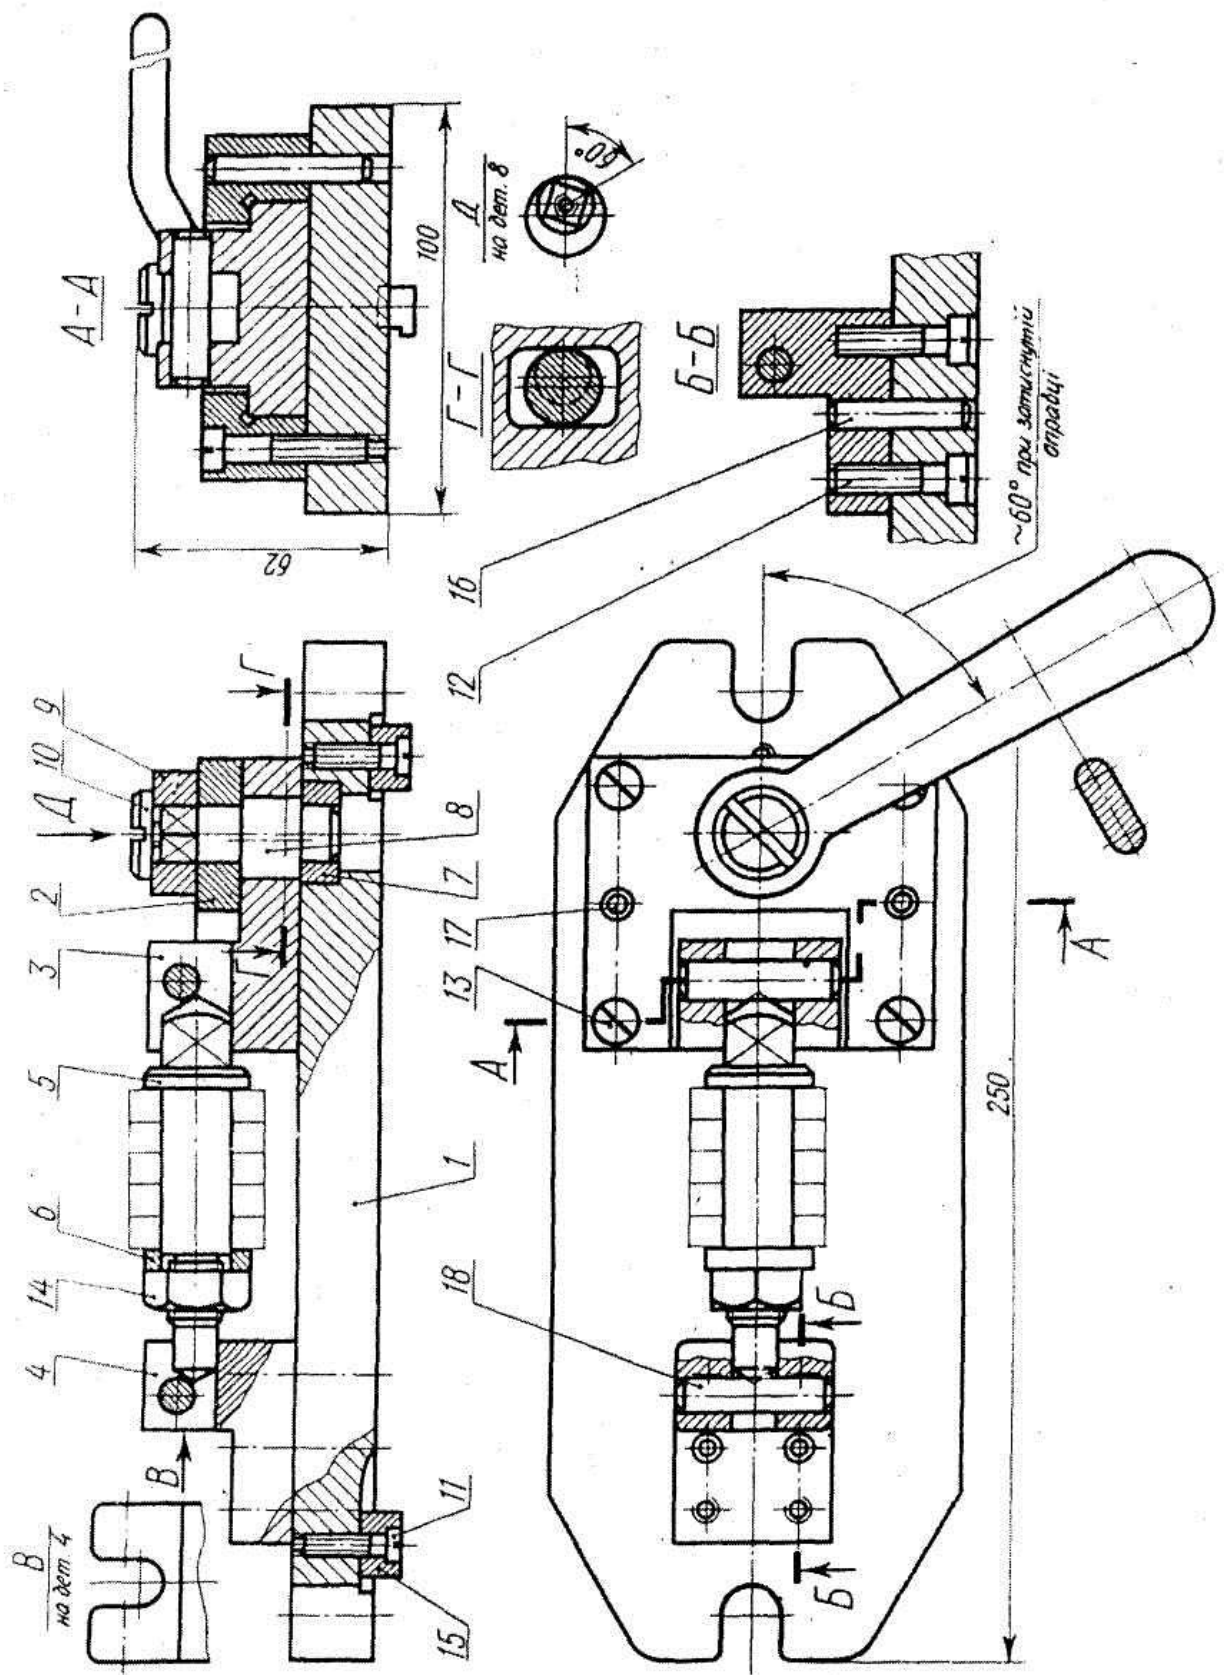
Пристрій для фрезерування пазів у круглих гайках
